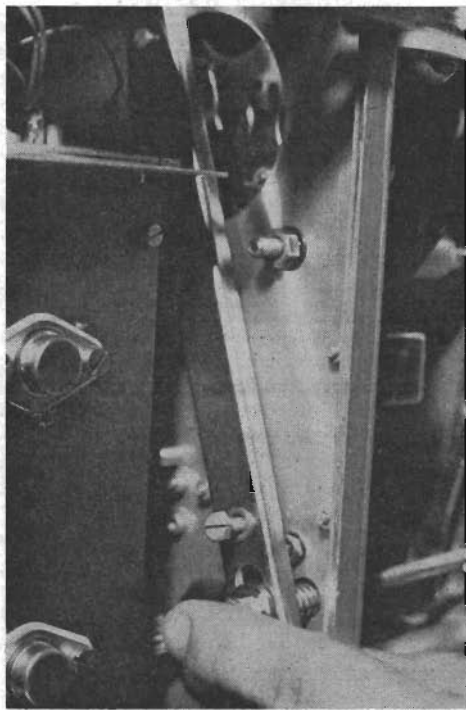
Sluttransistorerna — av RCA-tillverkning — har placerats utåt i chassieramen. Märk de bult- och skruvanslutna, grova stagen som ger stadga i olika dimensioner.
